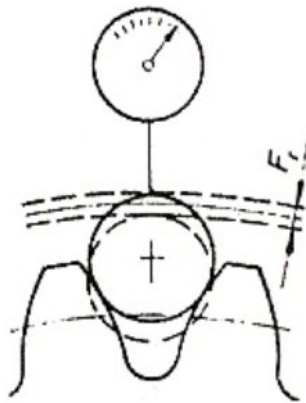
Místa kontroly házení ozubených kol po soustružení
